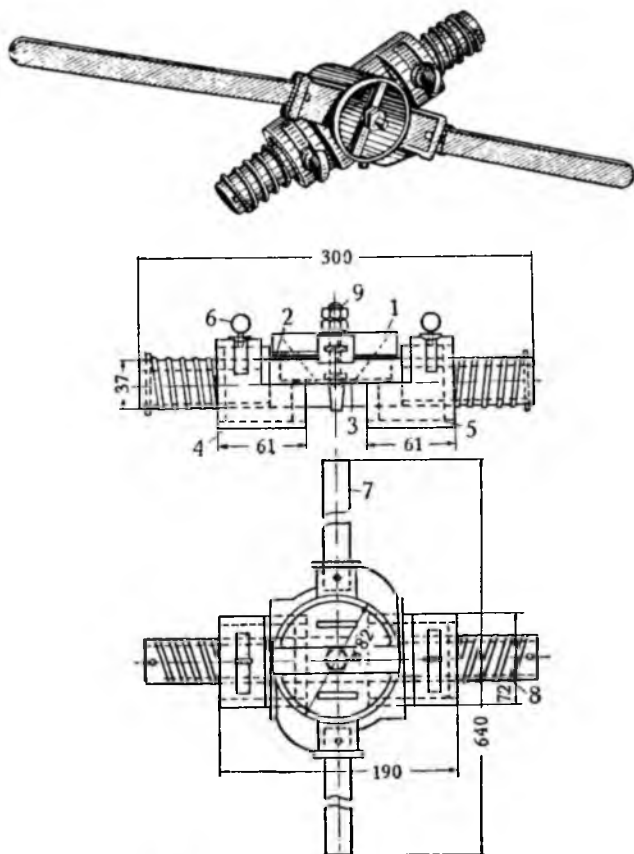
Общий вид и схема прибора для заливки коренных подшипников в блоках автомобилей ГАЗ:
